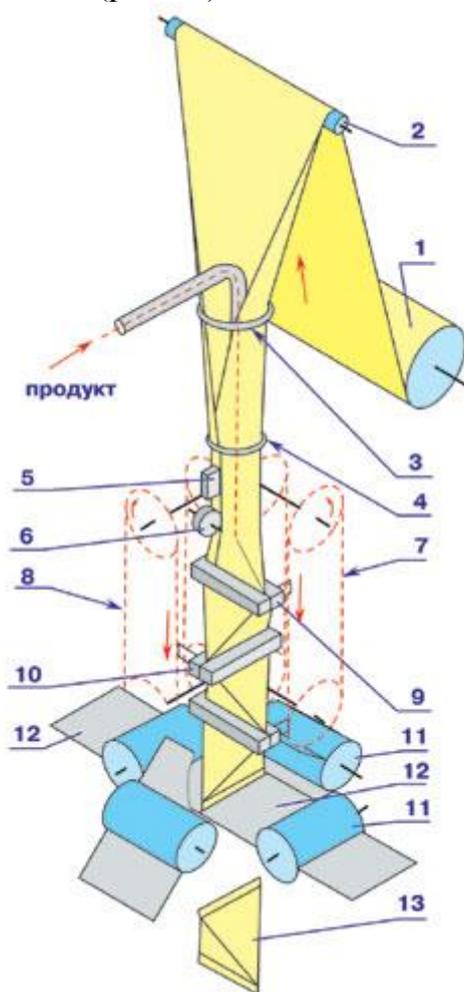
Схема безворотниковой упаковочной машины непрерывного действия с тянущими губками поперечной сварки, образующей пакет «тетра-классик»
